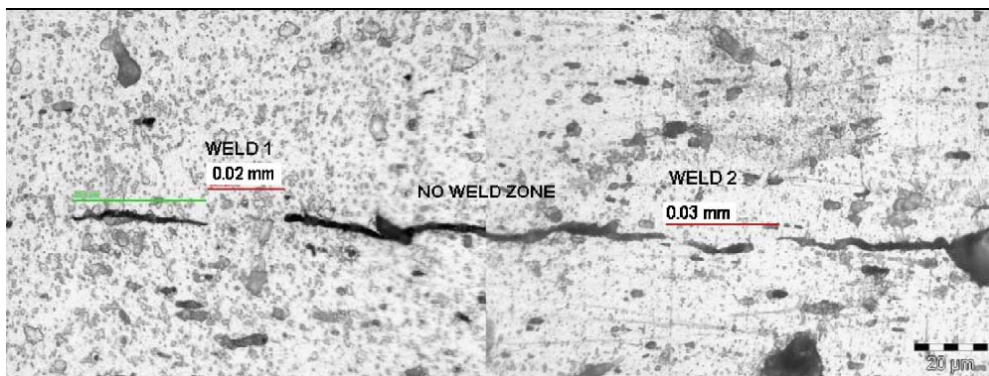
Microstructura unei îmbinări: weld 1, weld 2 – sudură; no weld zone – zona fără îmbinare (microstructur; pe sudură omogenă).
